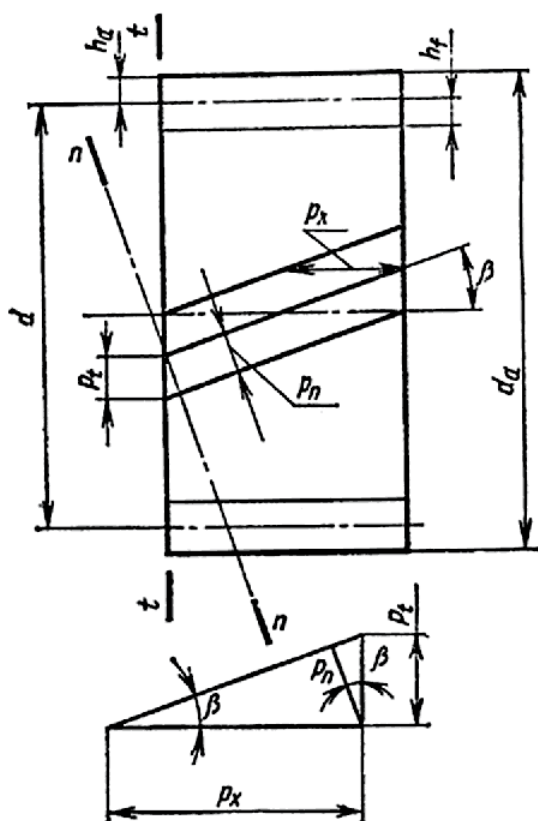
Элементы косозубой шестерни для настройки станка
